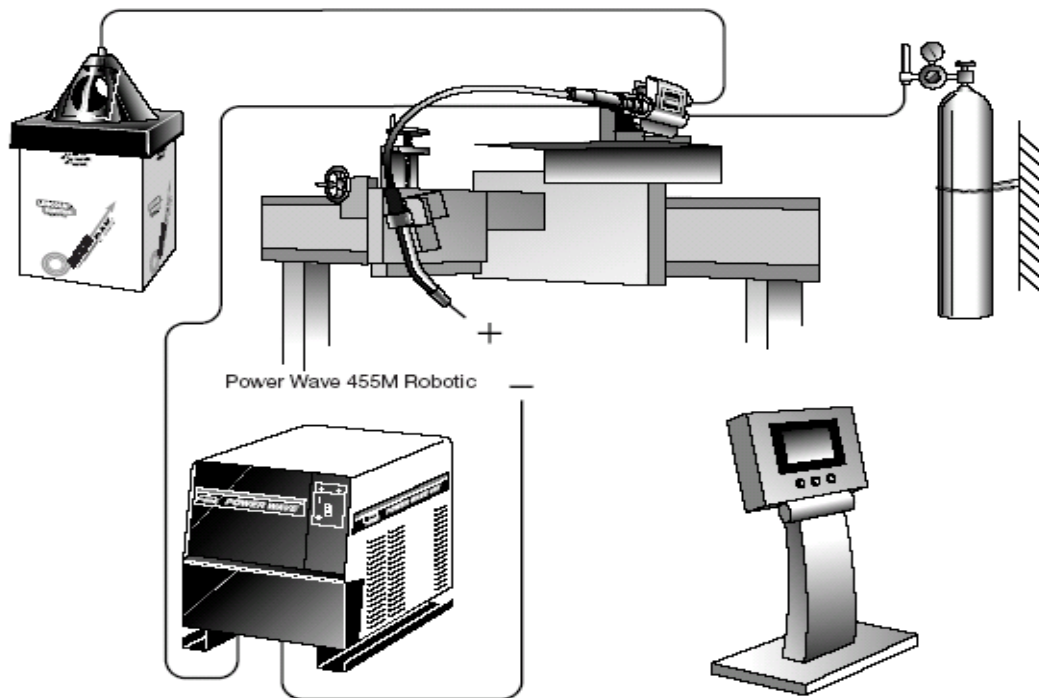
11 Principales componentes del equipo de soldadura GMAW automatizado (16).
